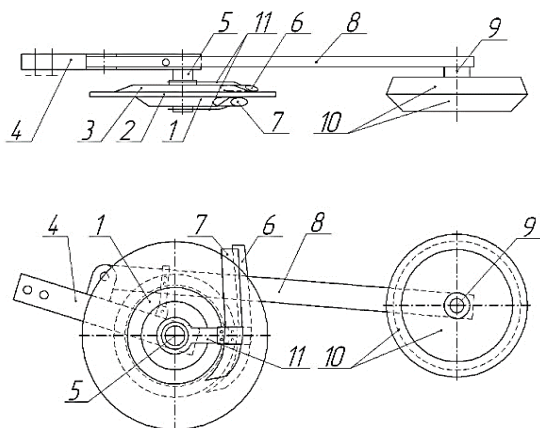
Комбинированный однодисковый сошник с двухсторонними ребрами-бороздкообразователями с разными диаметрами и нулевым углом атаки дисков: 1, 3 – реборды-бороздкообразователи; 2 – плоский диск; 4 – корпус; 5, 9 – оси; 6 – семянаправитель; 7 – туконаправитель; 8 – поводок; 10 – прикатывающий каток; 11 – пластины
